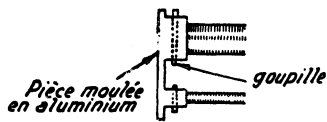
Raccord par pièce moulée goupillée sur les tubes
